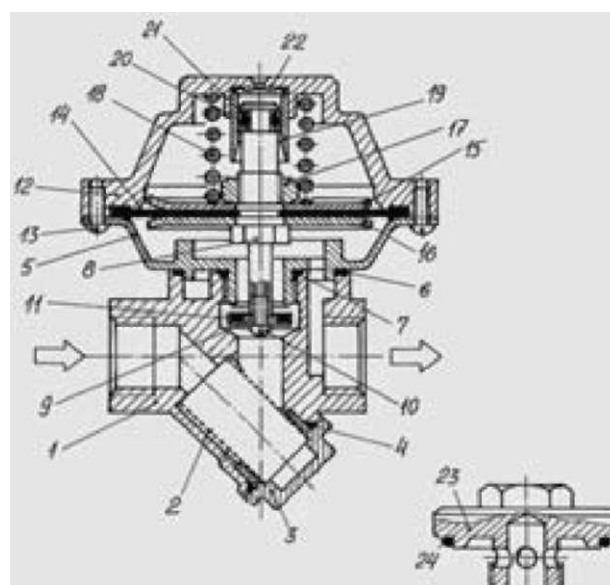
Принципиально-конструктивная схема квартирного мембранного редукционного клапана ФРД (1 — корпус клапана; 2 — фильтроэлемент; 3 — заглушка; 4 — уплотнительное эластичное кольцо; 5 — корпус седла клапана; 6 — уплотнительное эластичное кольцо; 7 — уплотнительное эластичное кольцо; 8 — шток; 9 — тарель клапана; 10 — винт; 11 — уплотнительная прокладка; 12 — крышка; 13 — крепежные винты; 14 — мембрана; 15 и 16 — опорные диски; 17 — гайка; 18 — пружина; 19 — втулка демпфера; 20 — упругое кольцо из эластичного материала; 21 — разрезная фторопластовая втулка; 22 — клапан гидравлического предохранителя от протечек)
